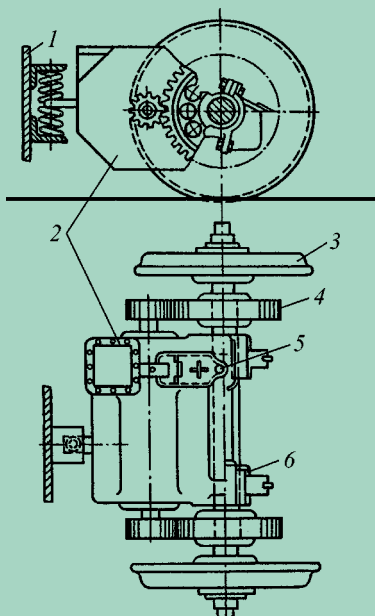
Опорно-осевая подвеска тягового двигателя: 1 — рама тележки; 2 — тяговый электродвигатель; 3 — колесная пара; 4 — зубчатая передача; 5 — моторно-осевые подшипники
